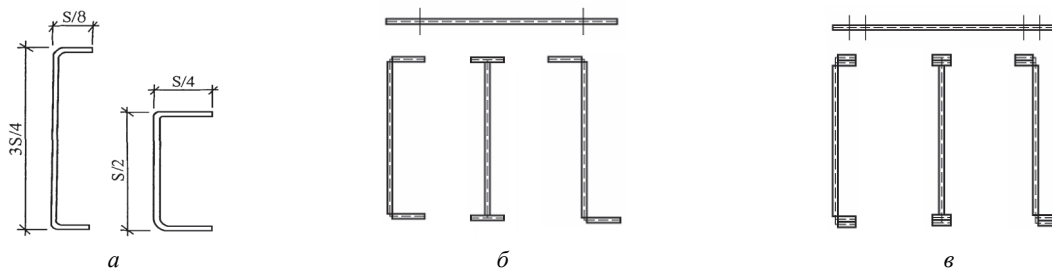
Схемы профилей и их заготовок с полками одинарной (а, б) и двойной (в) толщины
